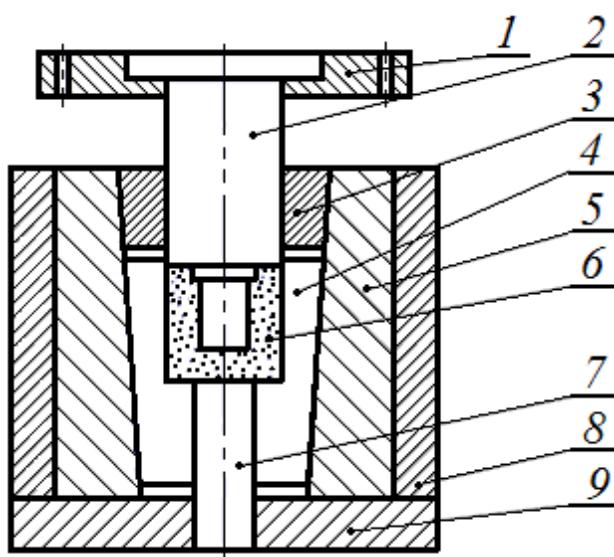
Схема опытной оснастки для выдавливания полости в профилированной заготовке, 1-пуансонодержатель, 2 – пуансон, 3- направляющая втулка, 4 – разъемная матрица, 5 – обойма, 6 – изделие, 7 – выталкиватель, 8 – бандаж, 9 – плита опорная.
